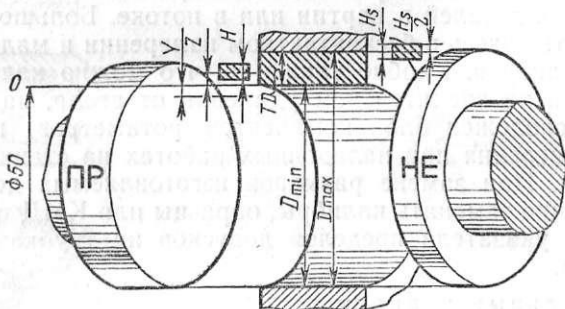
Схема полей допусков гладких калибров-пробок
